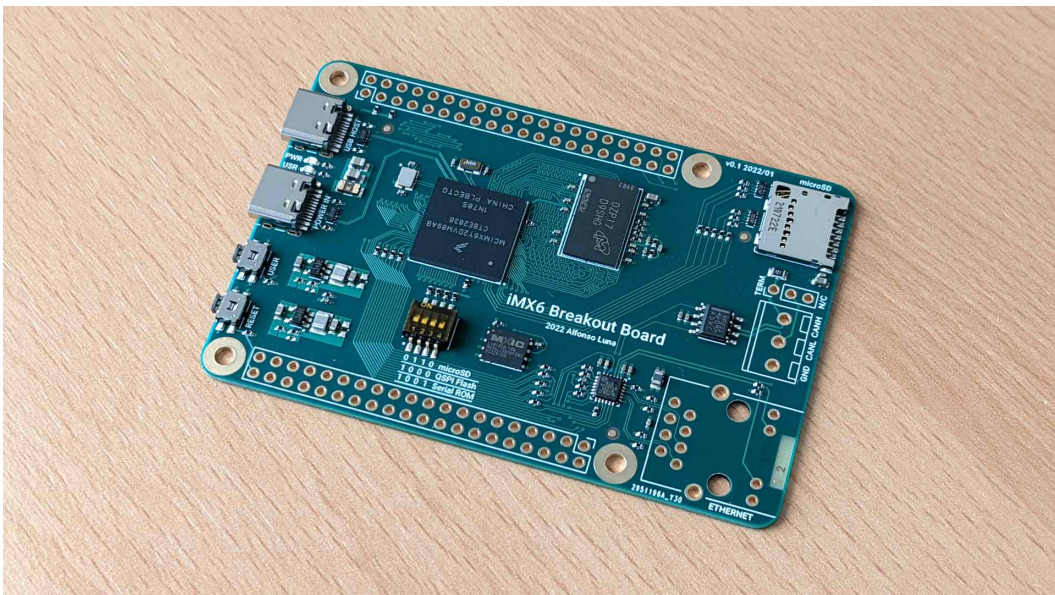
PCB tras soldar los componentes SMD de la cara superior.
